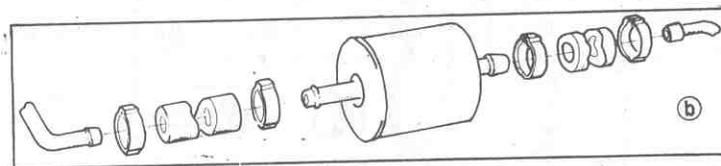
, detalle b.- Montaje del filtro de nafta entre la bomba y el carburador.
